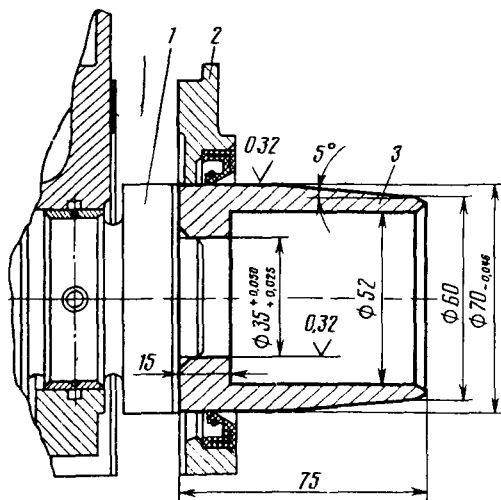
Установка держателя манжеты на фланец коленчатого вала:
